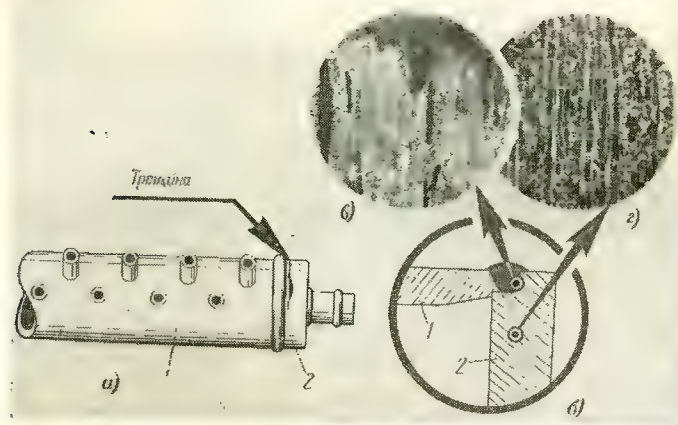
Трещина в плоском днище камеры пароперегревателя. а—вид конца камеры с трещиной, появившейся на границе кольцевого сварного шва; б—приварка днища 2 к цилиндрической части 1 камеры; в—трещины в металле; 2—структура металла днища (увеличено в 35 раз).
